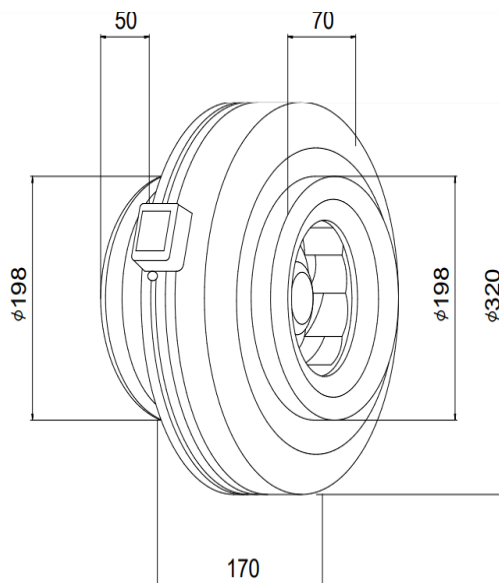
Чертёж общего вида канального вентилятора Soler Palau
